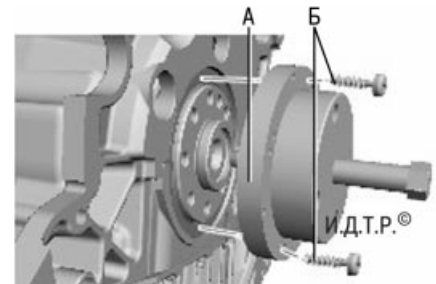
Установка заднего сальника коленчатого вала: А – приспособление для установки заднего уплотнения коленчатого вала; Б – винты крепления приспособления
